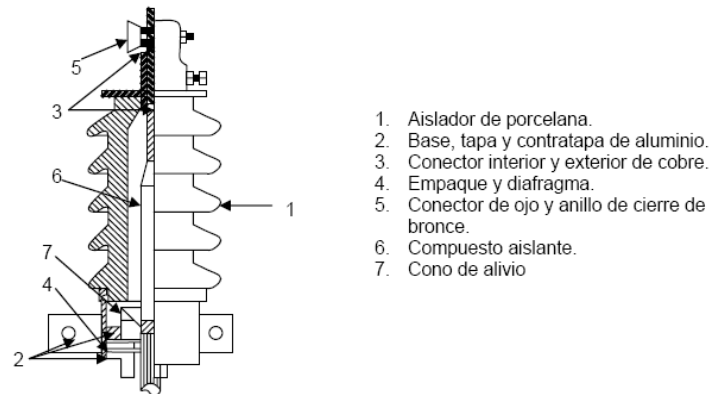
Detalle constructivo de la terminal tipo bayoneta instalada en cable con aislamiento extruído
